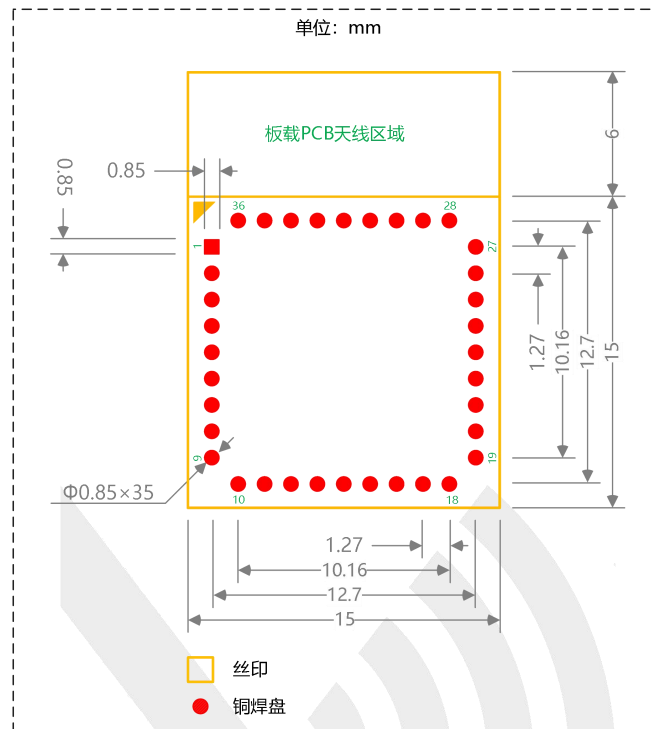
xmBLE-17H66B2-TP 推荐 PCB 封装尺寸
